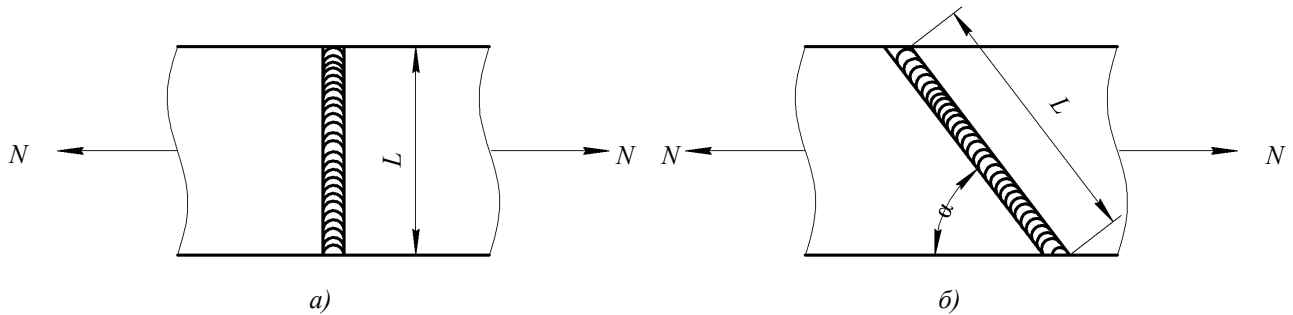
Типы сварных соединений: *a* — цилиндрическая соединяемая поверхность; *б* — коническая соединяемая поверхность; *N* — нагрузка; *L* — длина сварного шва; α — угол соединяемых поверхностей
